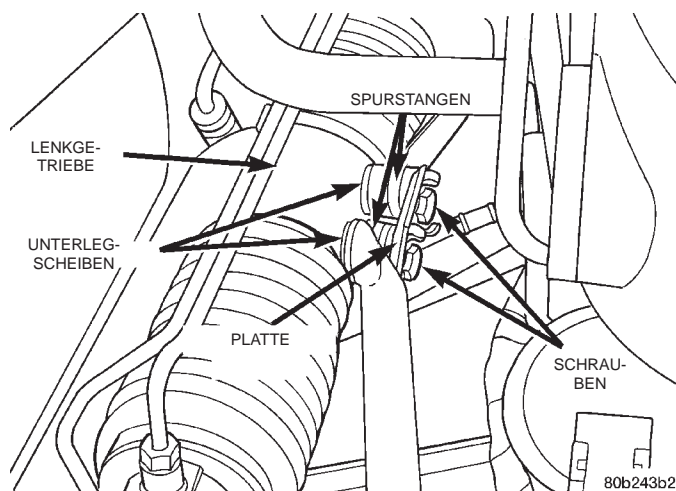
Befestigungsschrauben/Spurstangen an Lenkgetriebe
